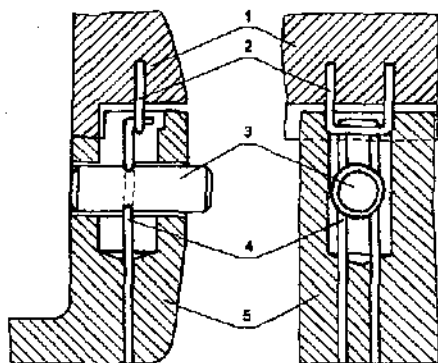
Замок для шкатулки: 1 — крышка; 2 — скоба для крышки; 3 — кнопка; 4 — запорная скоба; 5 — корпус
